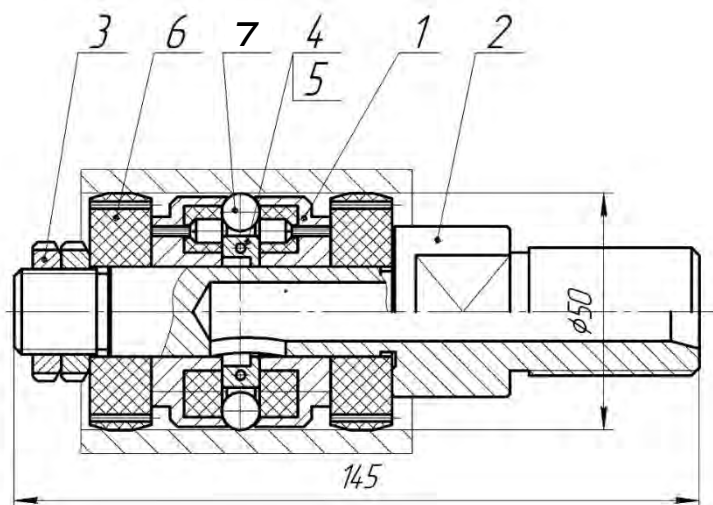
Конструктивная схема инструмента для упрочняющей обработки пневмоударом поверхностей отверстий
